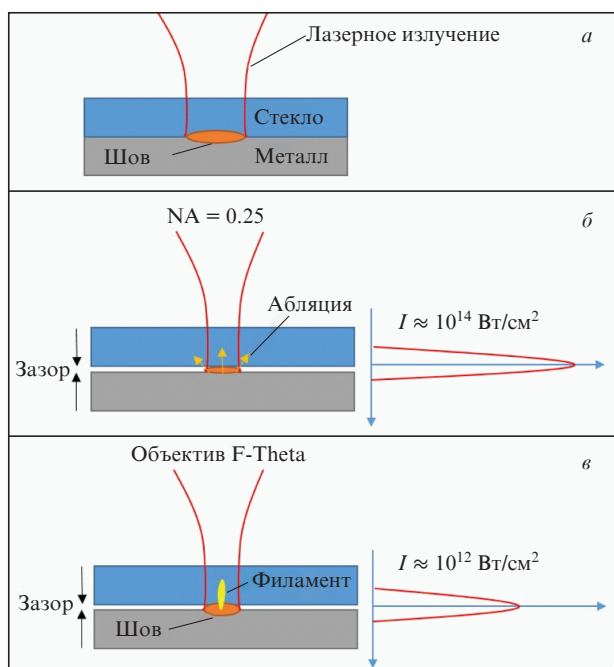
Схема образования сварных соединений стекло–металл.
